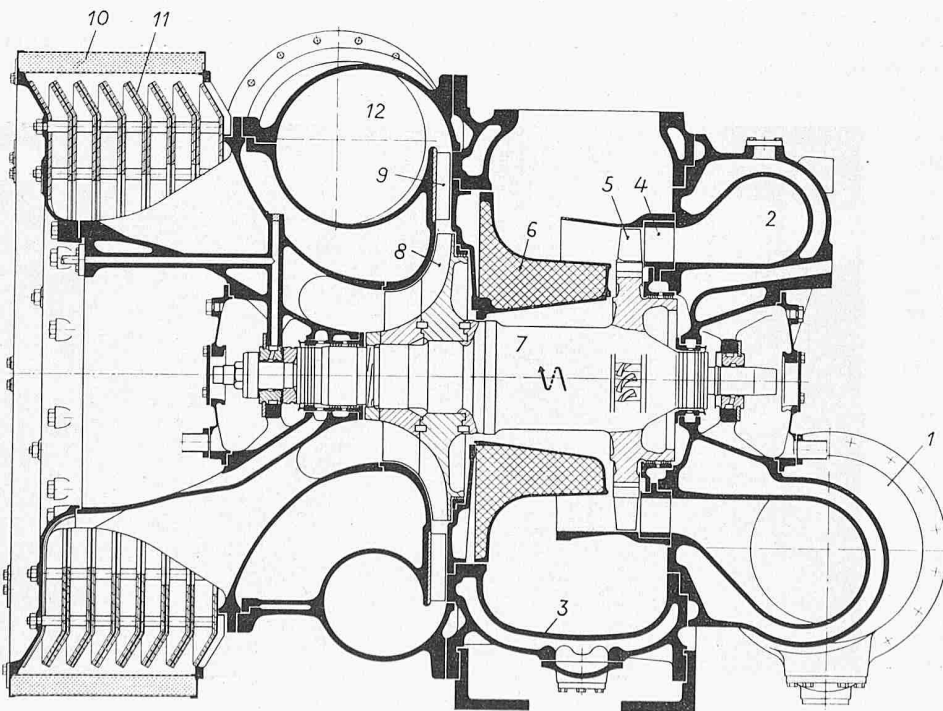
Sulzer-Abgasturbolader zum Motor 9 RSAD 76
